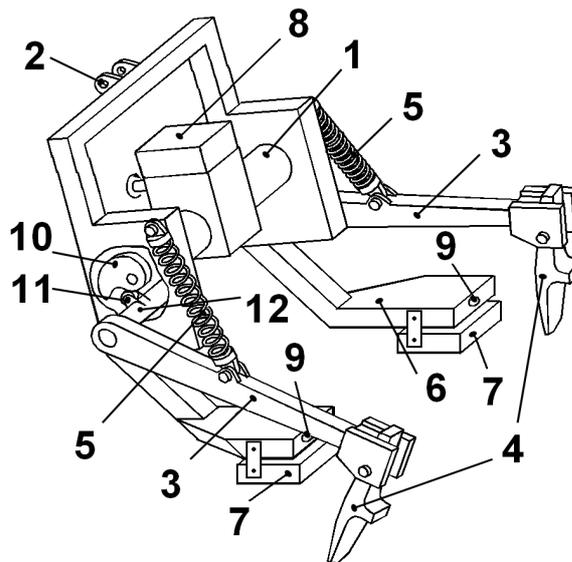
Лункообразователь с установленным пневматическим высевающим приспособлением [1]
